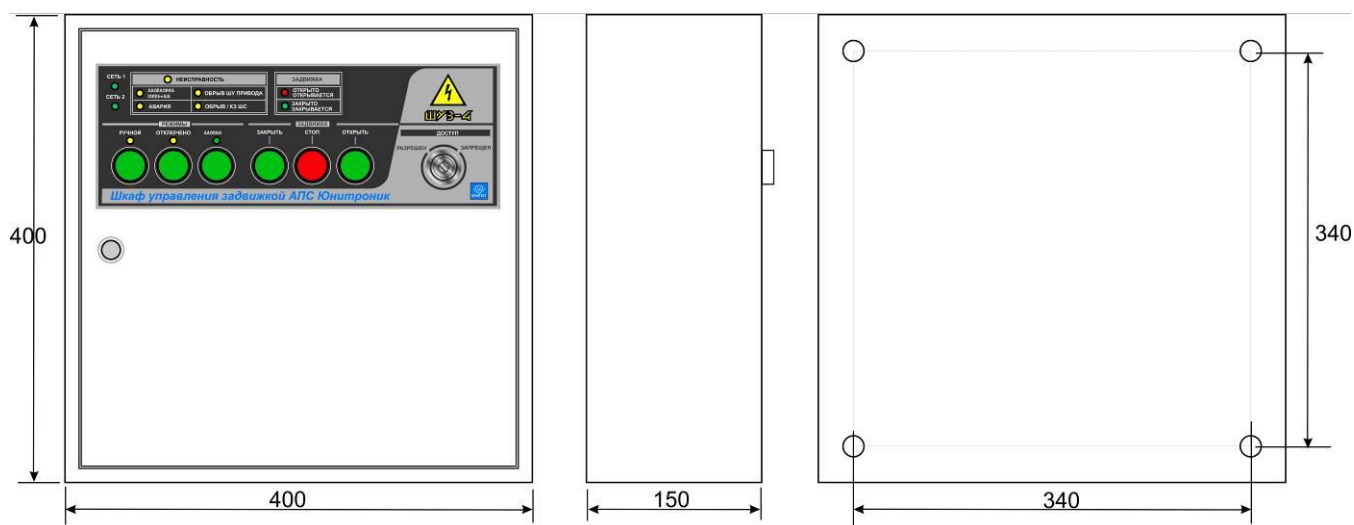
Габаритные и установочные размеры ШУЗ-4.
